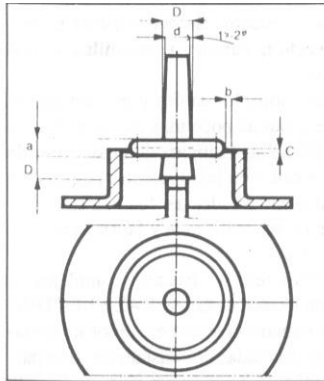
Inyección de diafragma. Adecuado para piezas cilíndricas que requieren buena concentricidad y una buena y resistente línea de unión de flujo (soldadura). Después del moldeo necesita una operación de corte del disco o diafragma. Se aconseja una longitud máxima de corte de 0.5 a 1 mm.
